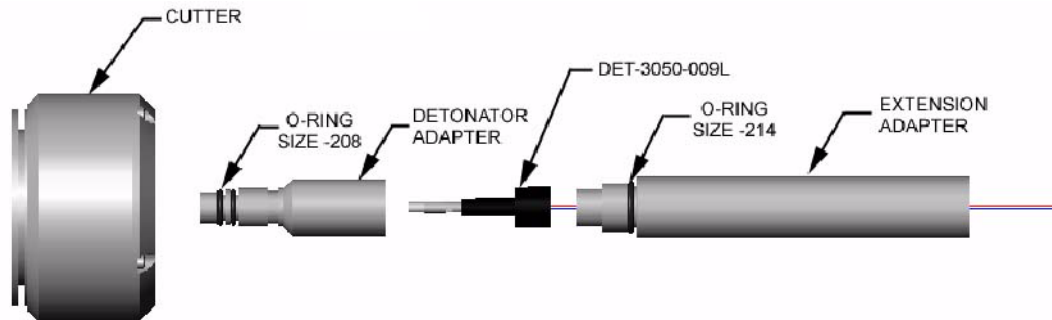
Méthode d'armement des coupe-tiges NT Casing Cutter - Vue éclatée
